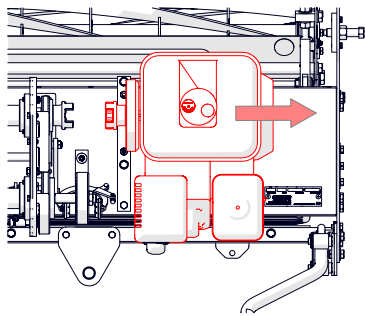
C – Faça deslizar o motor para fora do acoplamento.
